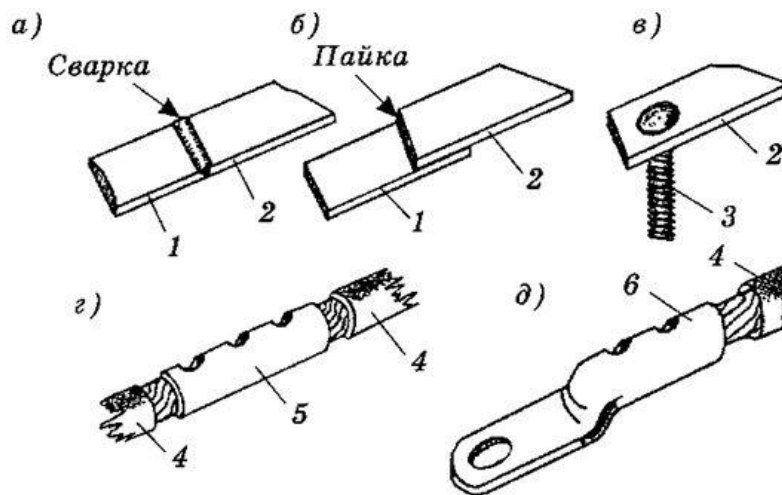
Неразборные контактные соединения: а – сваркой; б – пайкой; в – сваркой со штыревым выводом; г – опрессовкой через соединительную гильзу; д – опрессовкой с кабельным наконечником.
